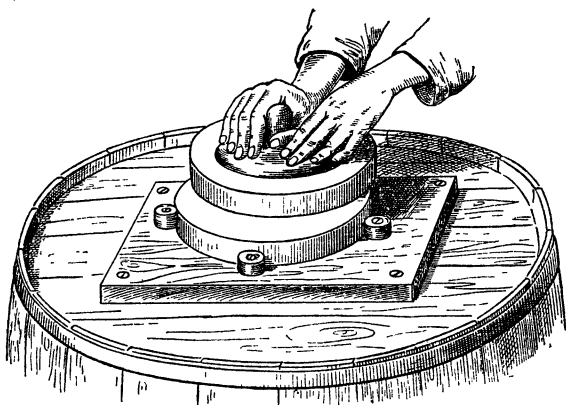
Шлифовка зеркала; шлифовальный диск укреплен на бочке с помощью четырех шурупов, пропущенных сквозь пробки (по А. А. Чикину; 1915).
